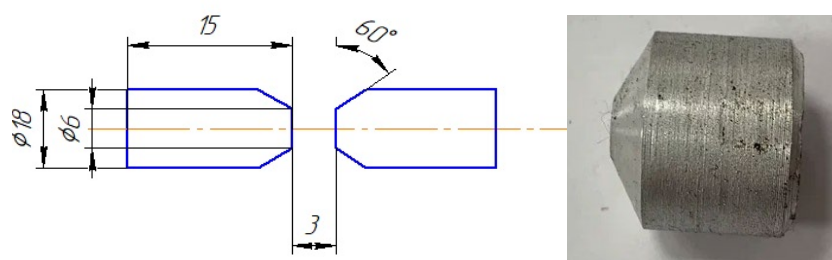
Образцы для проведения TIG сварки
